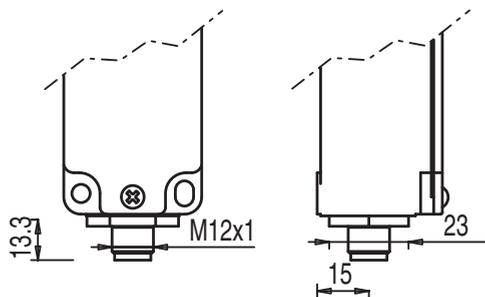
Dimensions du S200-M4C1-M12 en mm (dimensions du connecteur M12)
